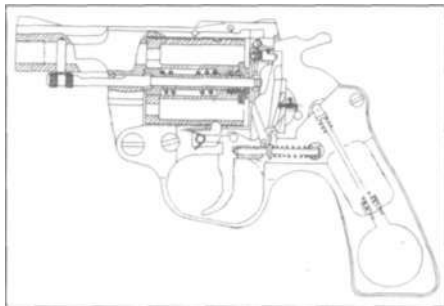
Prototyp 9 mm rewolweru gazowego konstrukcji Widzewskiej Fabryki Maszyn Włókienniczych w Łodzi
